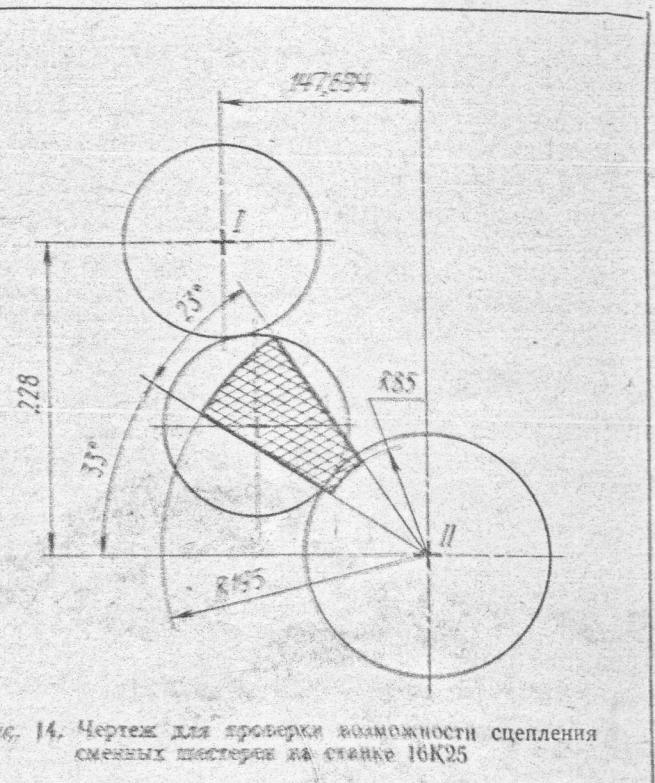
Чертеж для проверки возможности сцепления сменных шестерен на станке 16К25
